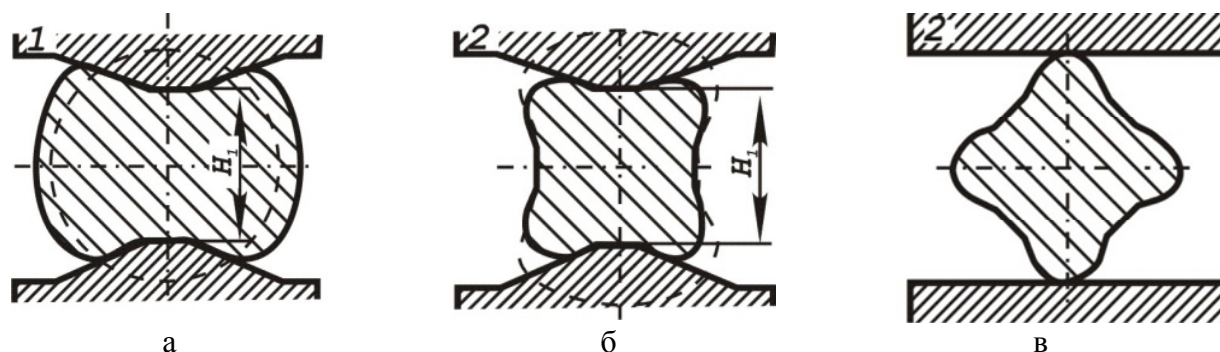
Последовательность получения четырехлучевой заготовки (а, б) и схема обкатки четырехлучевой заготовки на круглое сечение плоскими бойками (в)
